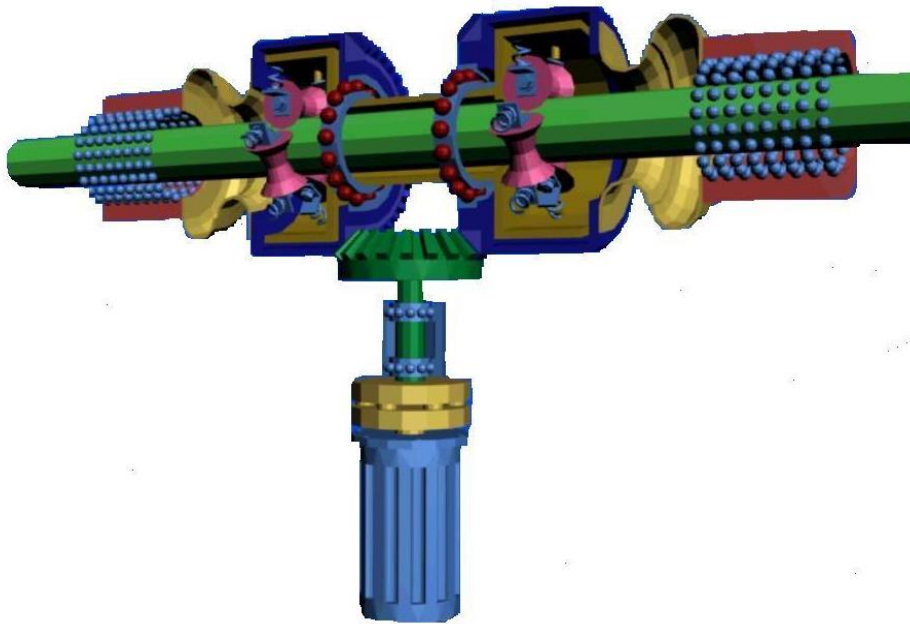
3D модель зміцнювача для поверхневого пластичного деформування торсіонних валів та зовнішніх поверхонь циліндричних довгомірних деталей.
